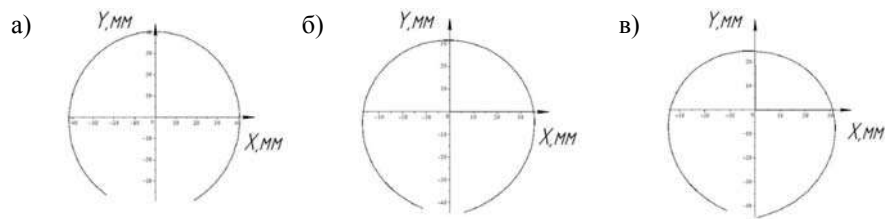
Сечения инструментальной поверхности фрезы для обработки наружной поверхности на длине: а) 30 мм; б) 180 мм; в) 330 мм.
